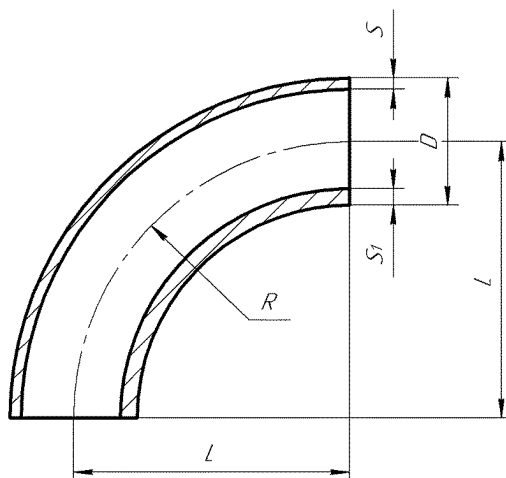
Разнотолщинность заготовки перед механической обработкой под сварку:
